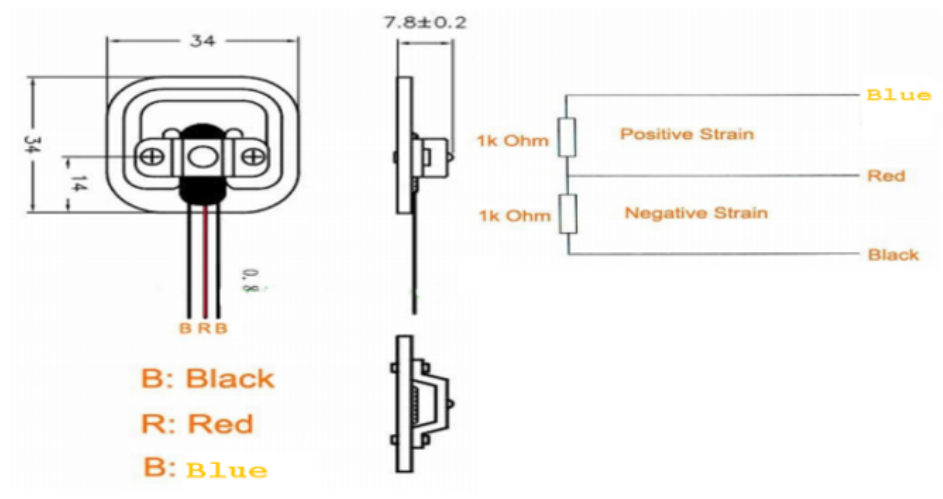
Dimensiones de celda de carga seleccionada. [38]
